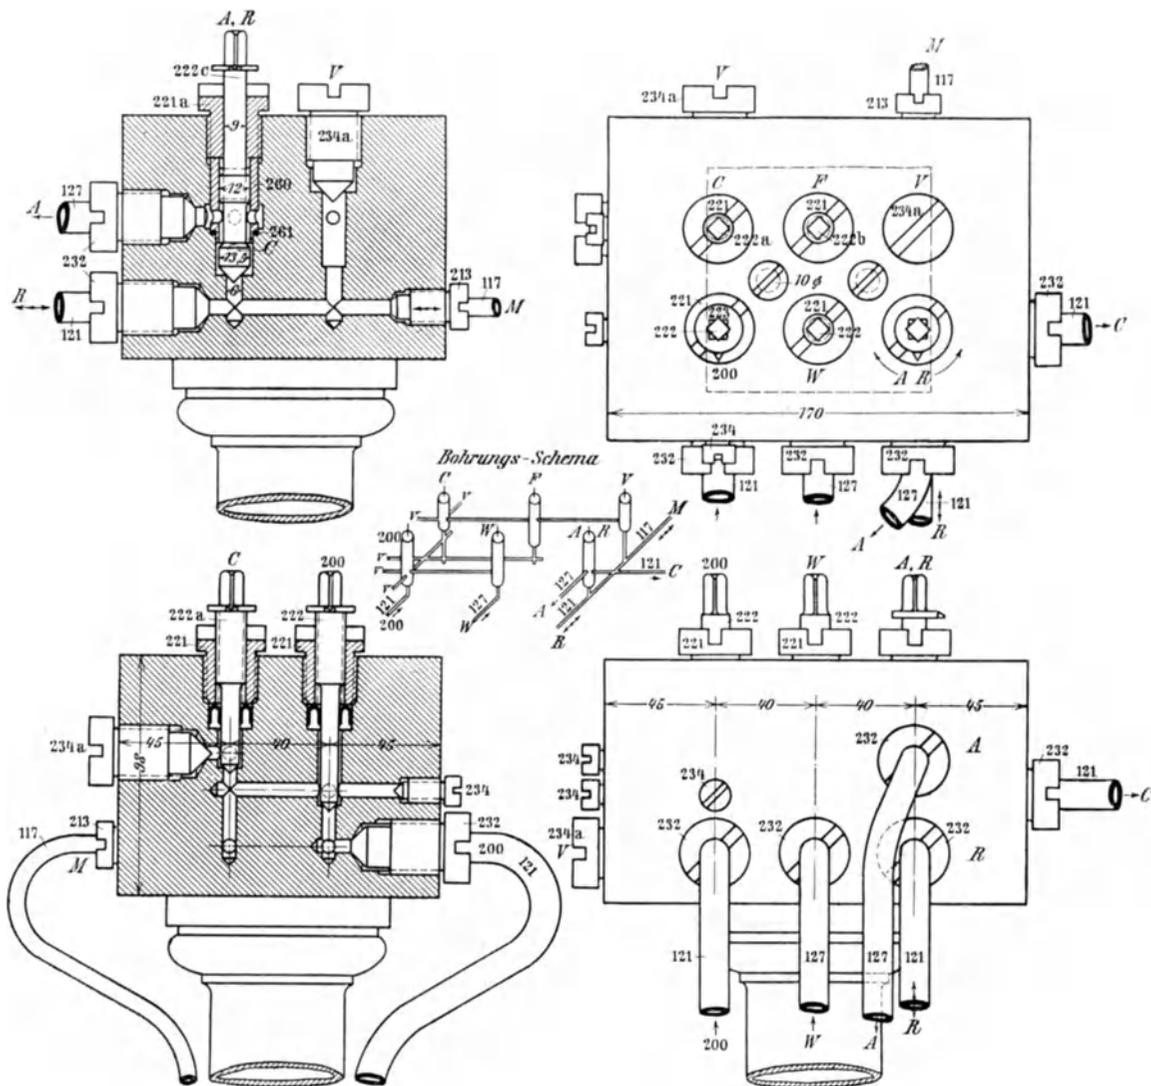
Steuerung der Werder- und Martens-Maschinen.
